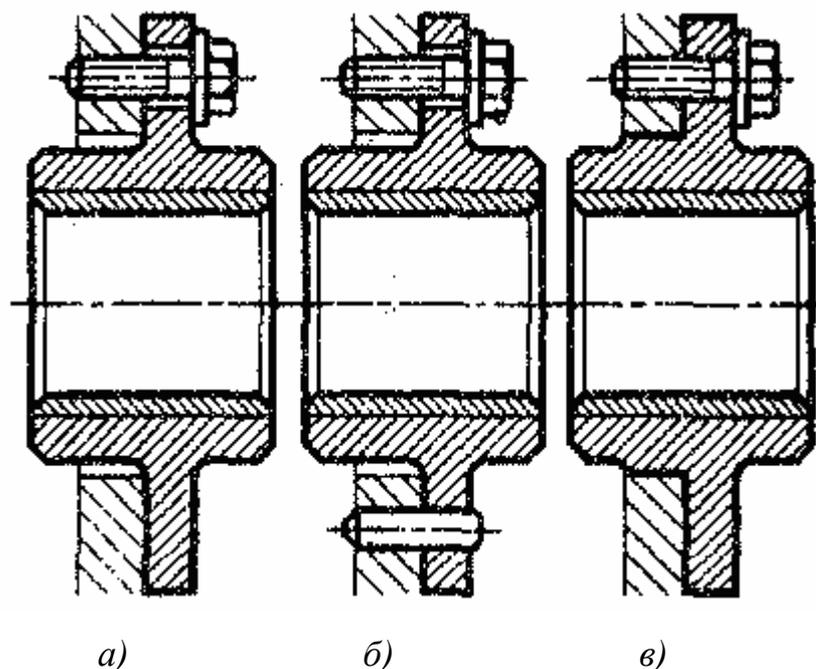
Устранение подгонки при установке подшипника в корпус
